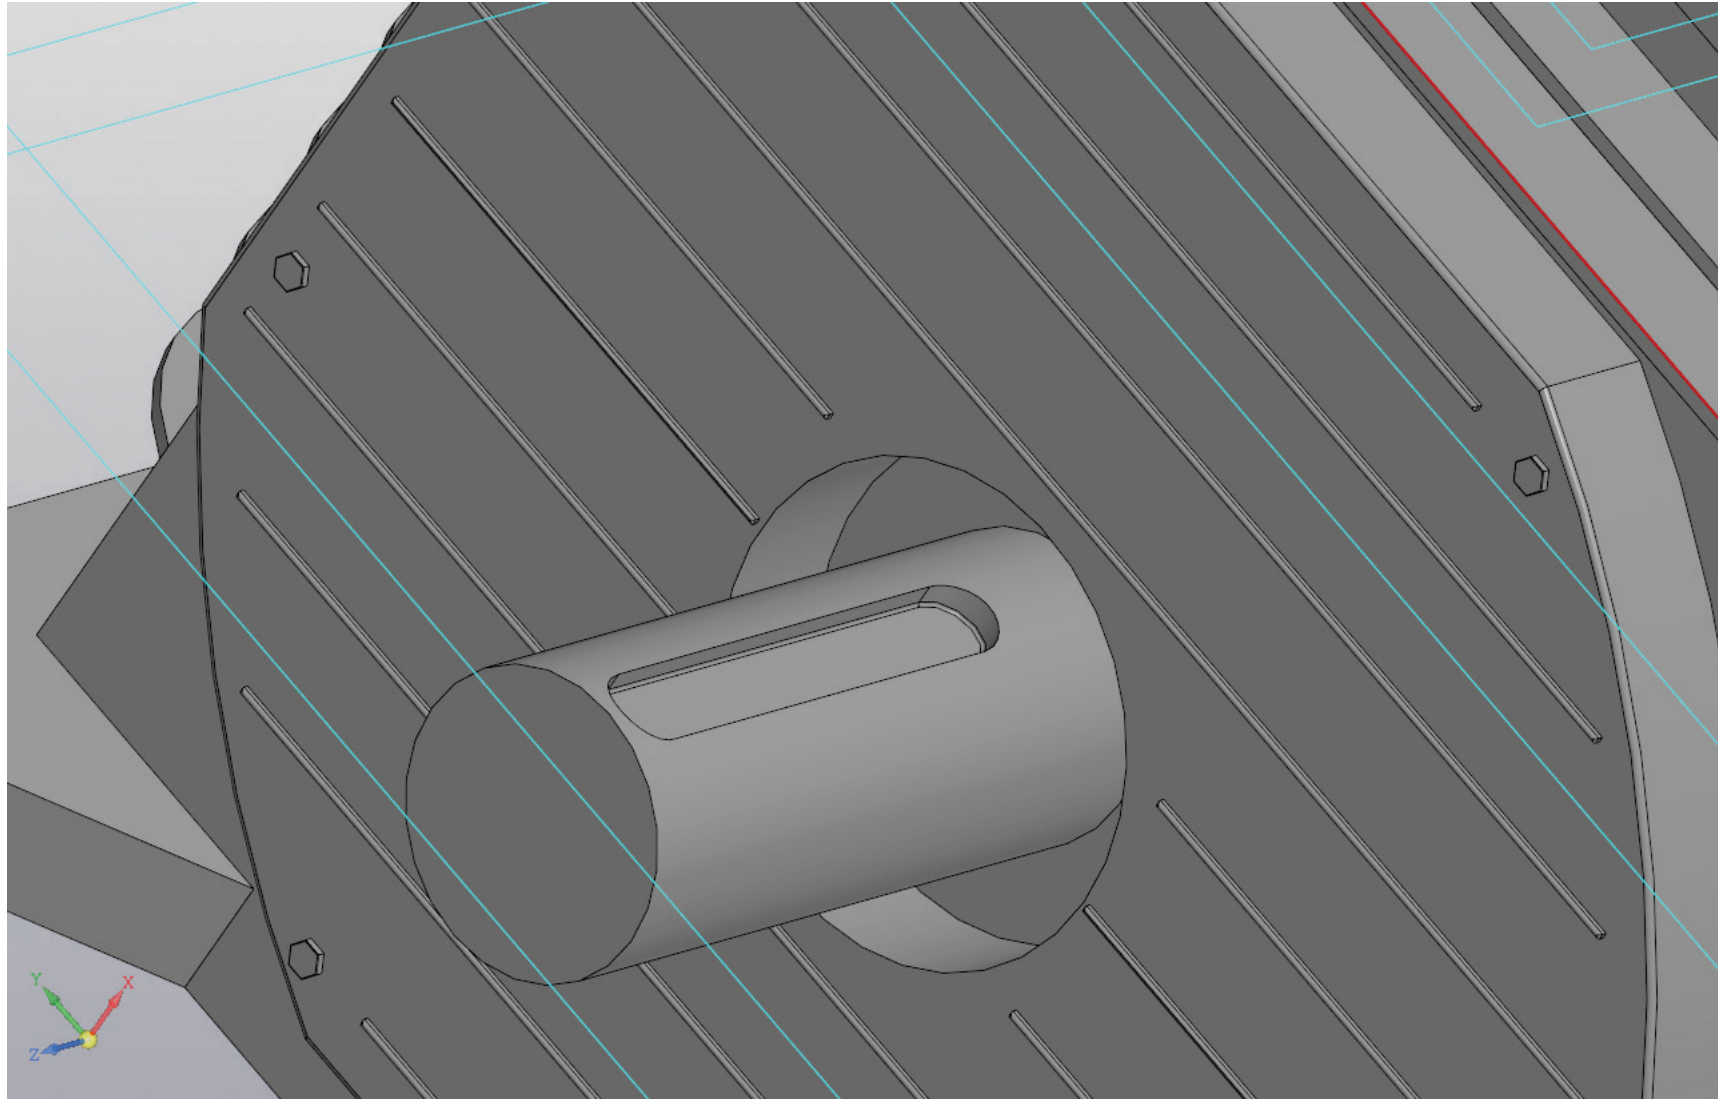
Шпоночная канавка на выходном валу редуктора
